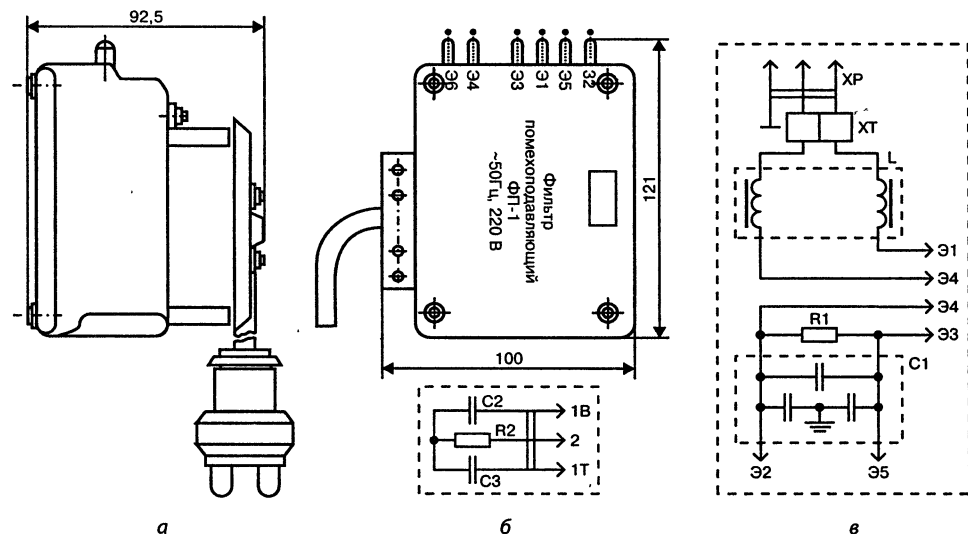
Внешний вид и схемные решения помехоподавляющих фильтров: а — внешний вид; б — искрогасящий контур; в — фильтр питания комбинированный
